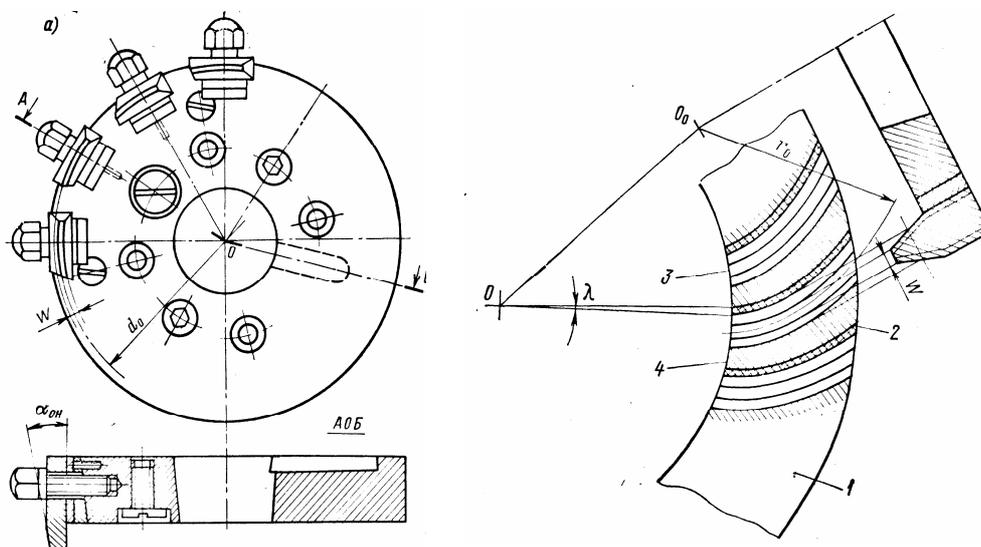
Двухсторонняя резцовая головка и схема поворотного одностороннего метода нарезания зубьев конического зубчатого колеса:
